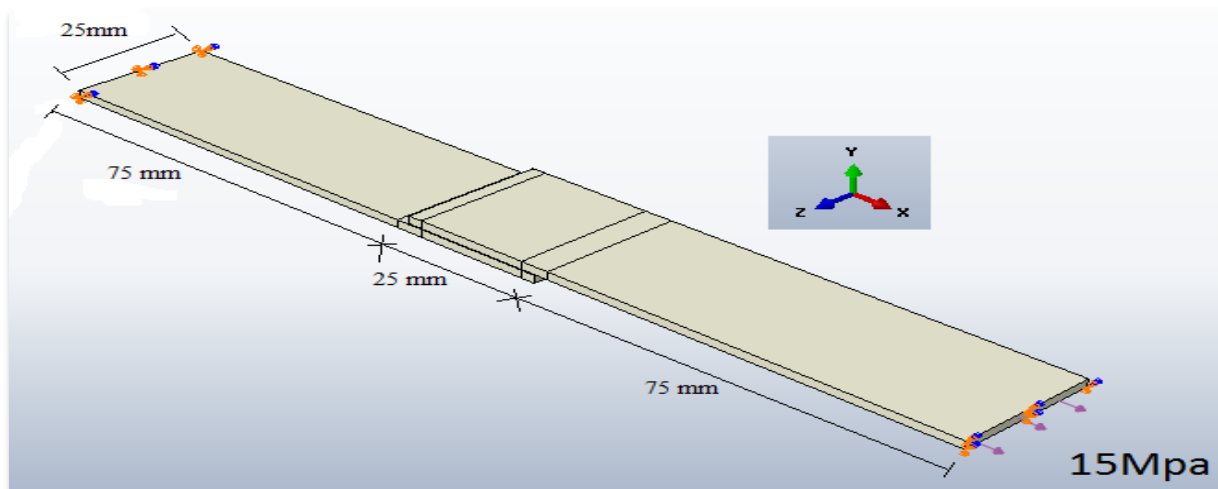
géométrie et dimensions du modèle simple recouvrement.
